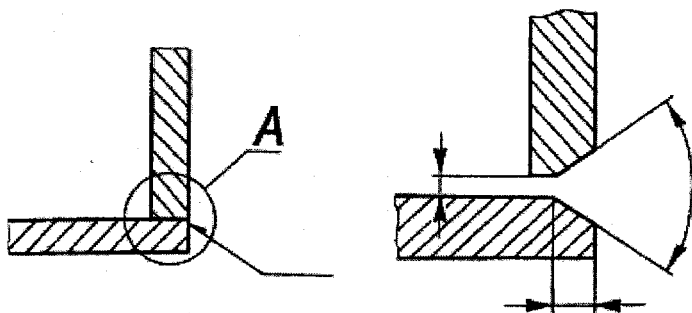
Пример изображения разделки кромок свариваемых деталей
